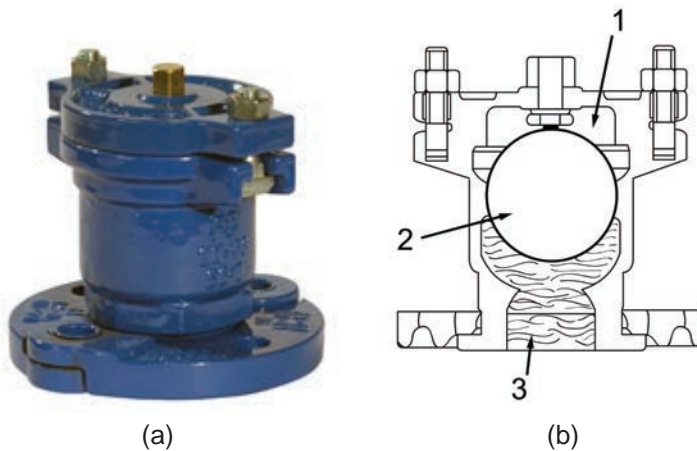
Detalhe de uma ventosa de simples função – (a) vista geral – (b) corte esquemático
